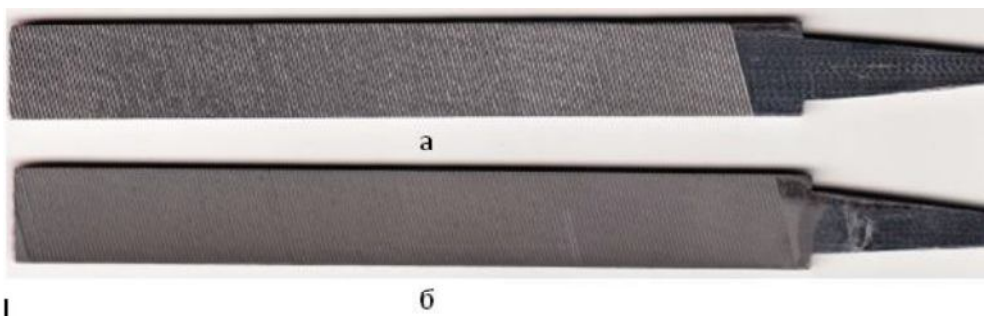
Напильник с фрезерованными зубьями до напыления (а) и после напыления твердого сплава (б)
